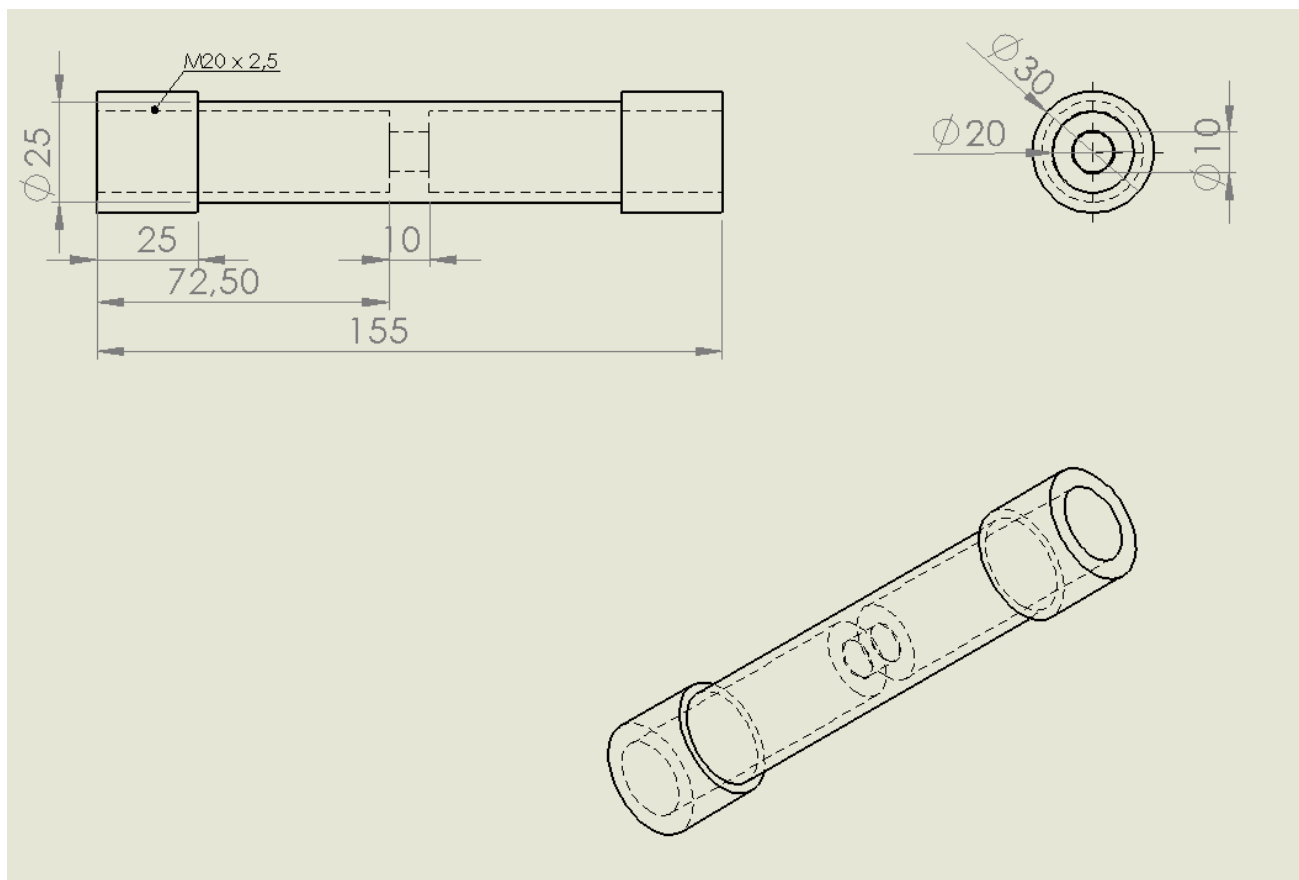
A_ PLANO ELEMENTO COBERTURA
